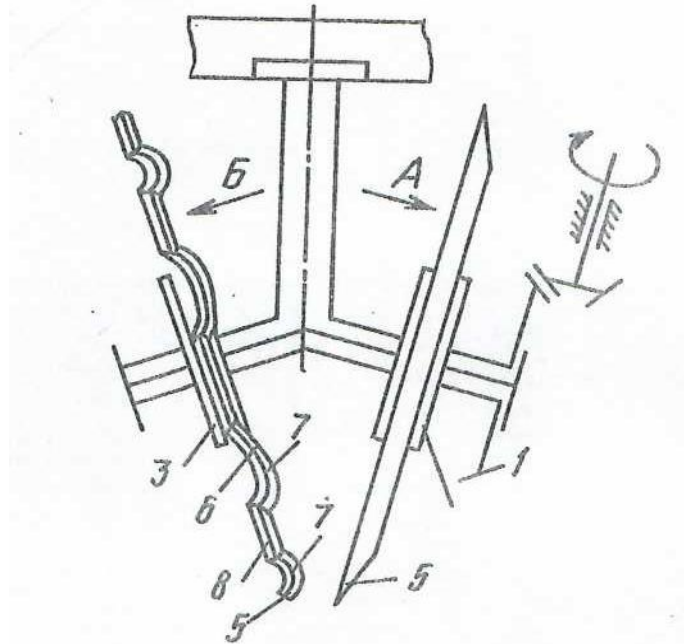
Пристрій для викопування коренеплодів [12], вид спереду
